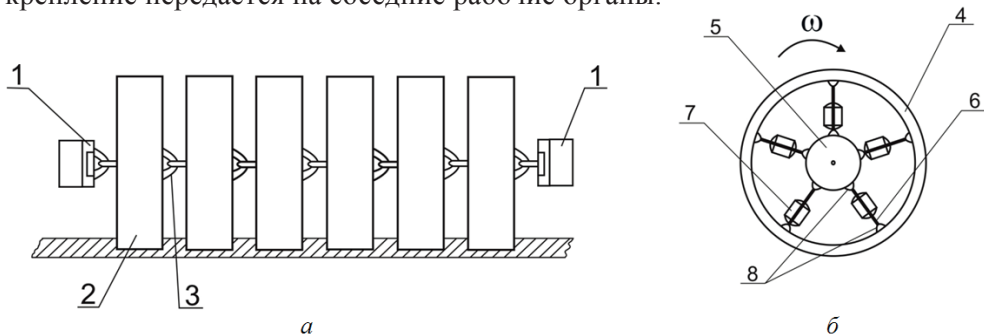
Шарнирно-ударный почвообрабатывающий каток: а – общий вид катка, б – катковое звено. 1 – подшипниковый узел, 2 – катковое звено, 3 – крестообразный шарнир, 4 – пустотелый диск, 5 – кольцо, 6 – спица, 7 – цилиндрический ударник, 8 – полусферовая наковальня
